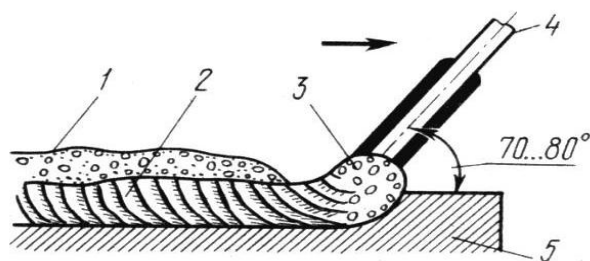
Сварка с глубоким проплавлением
